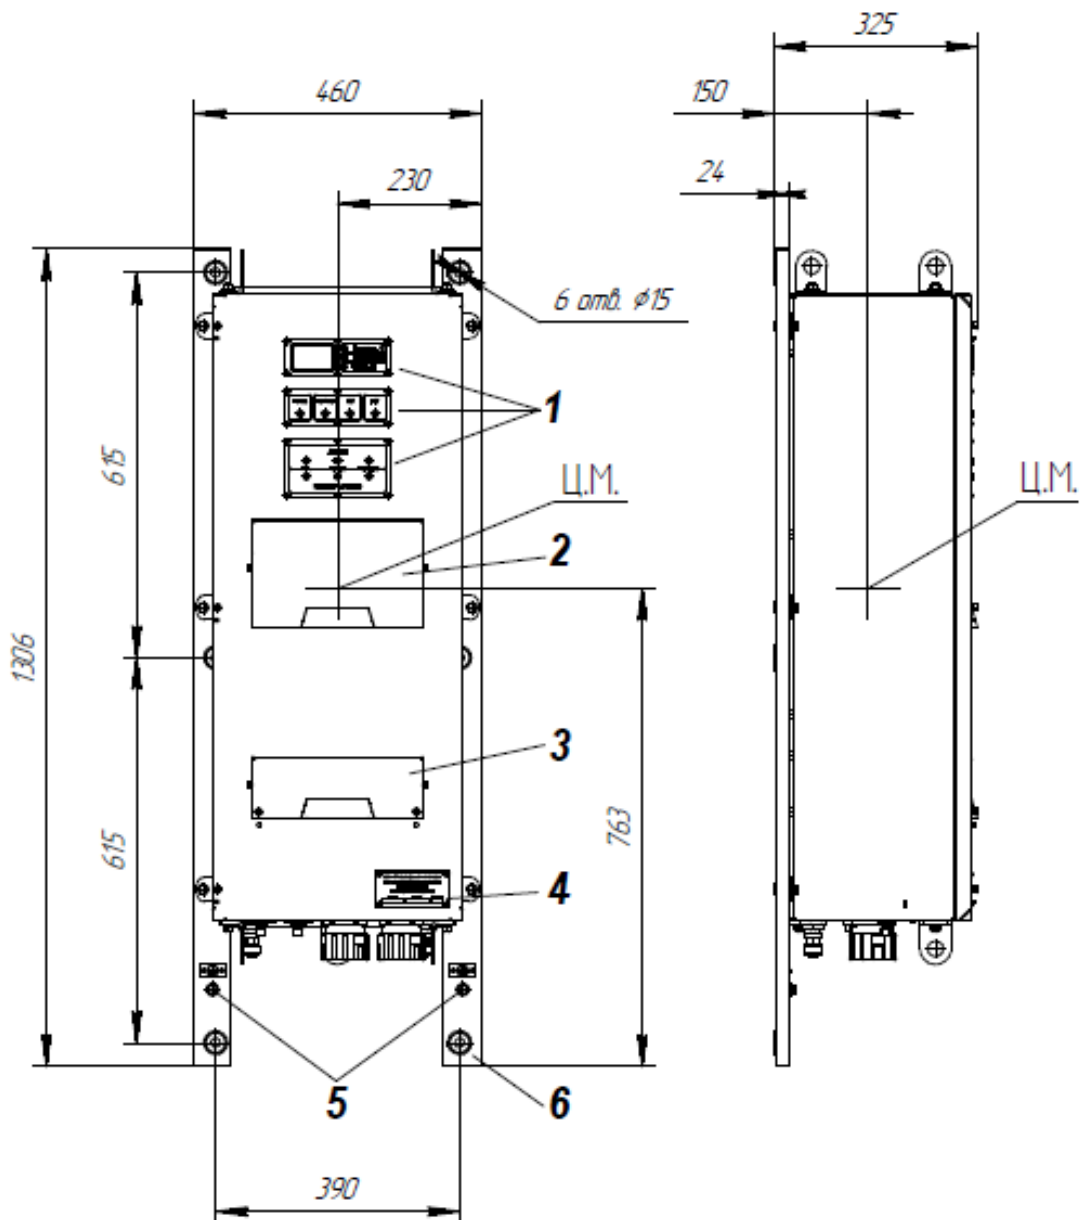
Внешний вид МПЧ-380-11-14
